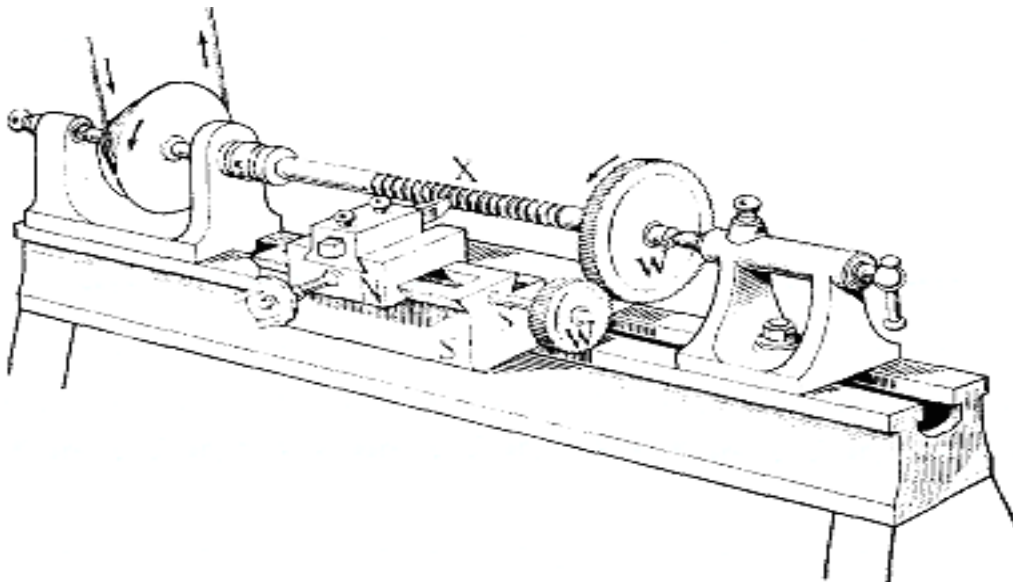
Принцип устройства токарно-винторезного станка (рисунок Дж. Несмита, 1841 г.)
